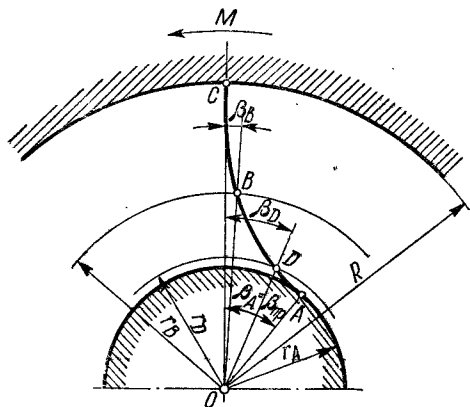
Схема испытания на скручивание плоской заготовки (по Марчиньяку)
